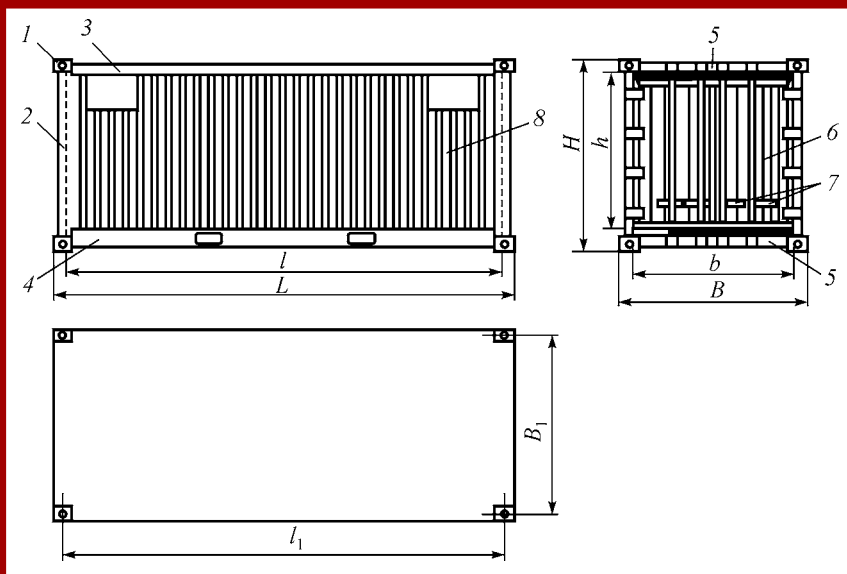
Общий вид и конструкция крупнотоннажного контейнера: 1 — фитинг; 2 — вертикальная (угловая) стойка; 3 — верхняя продольная балка; 4 — нижняя продольная балка с пазами для вилочного захвата; 5 — торцовые (верхняя и нижняя) балки; 6 — дверные створки; 7 — механизмы запора дверей; 8 — боковые стенки
